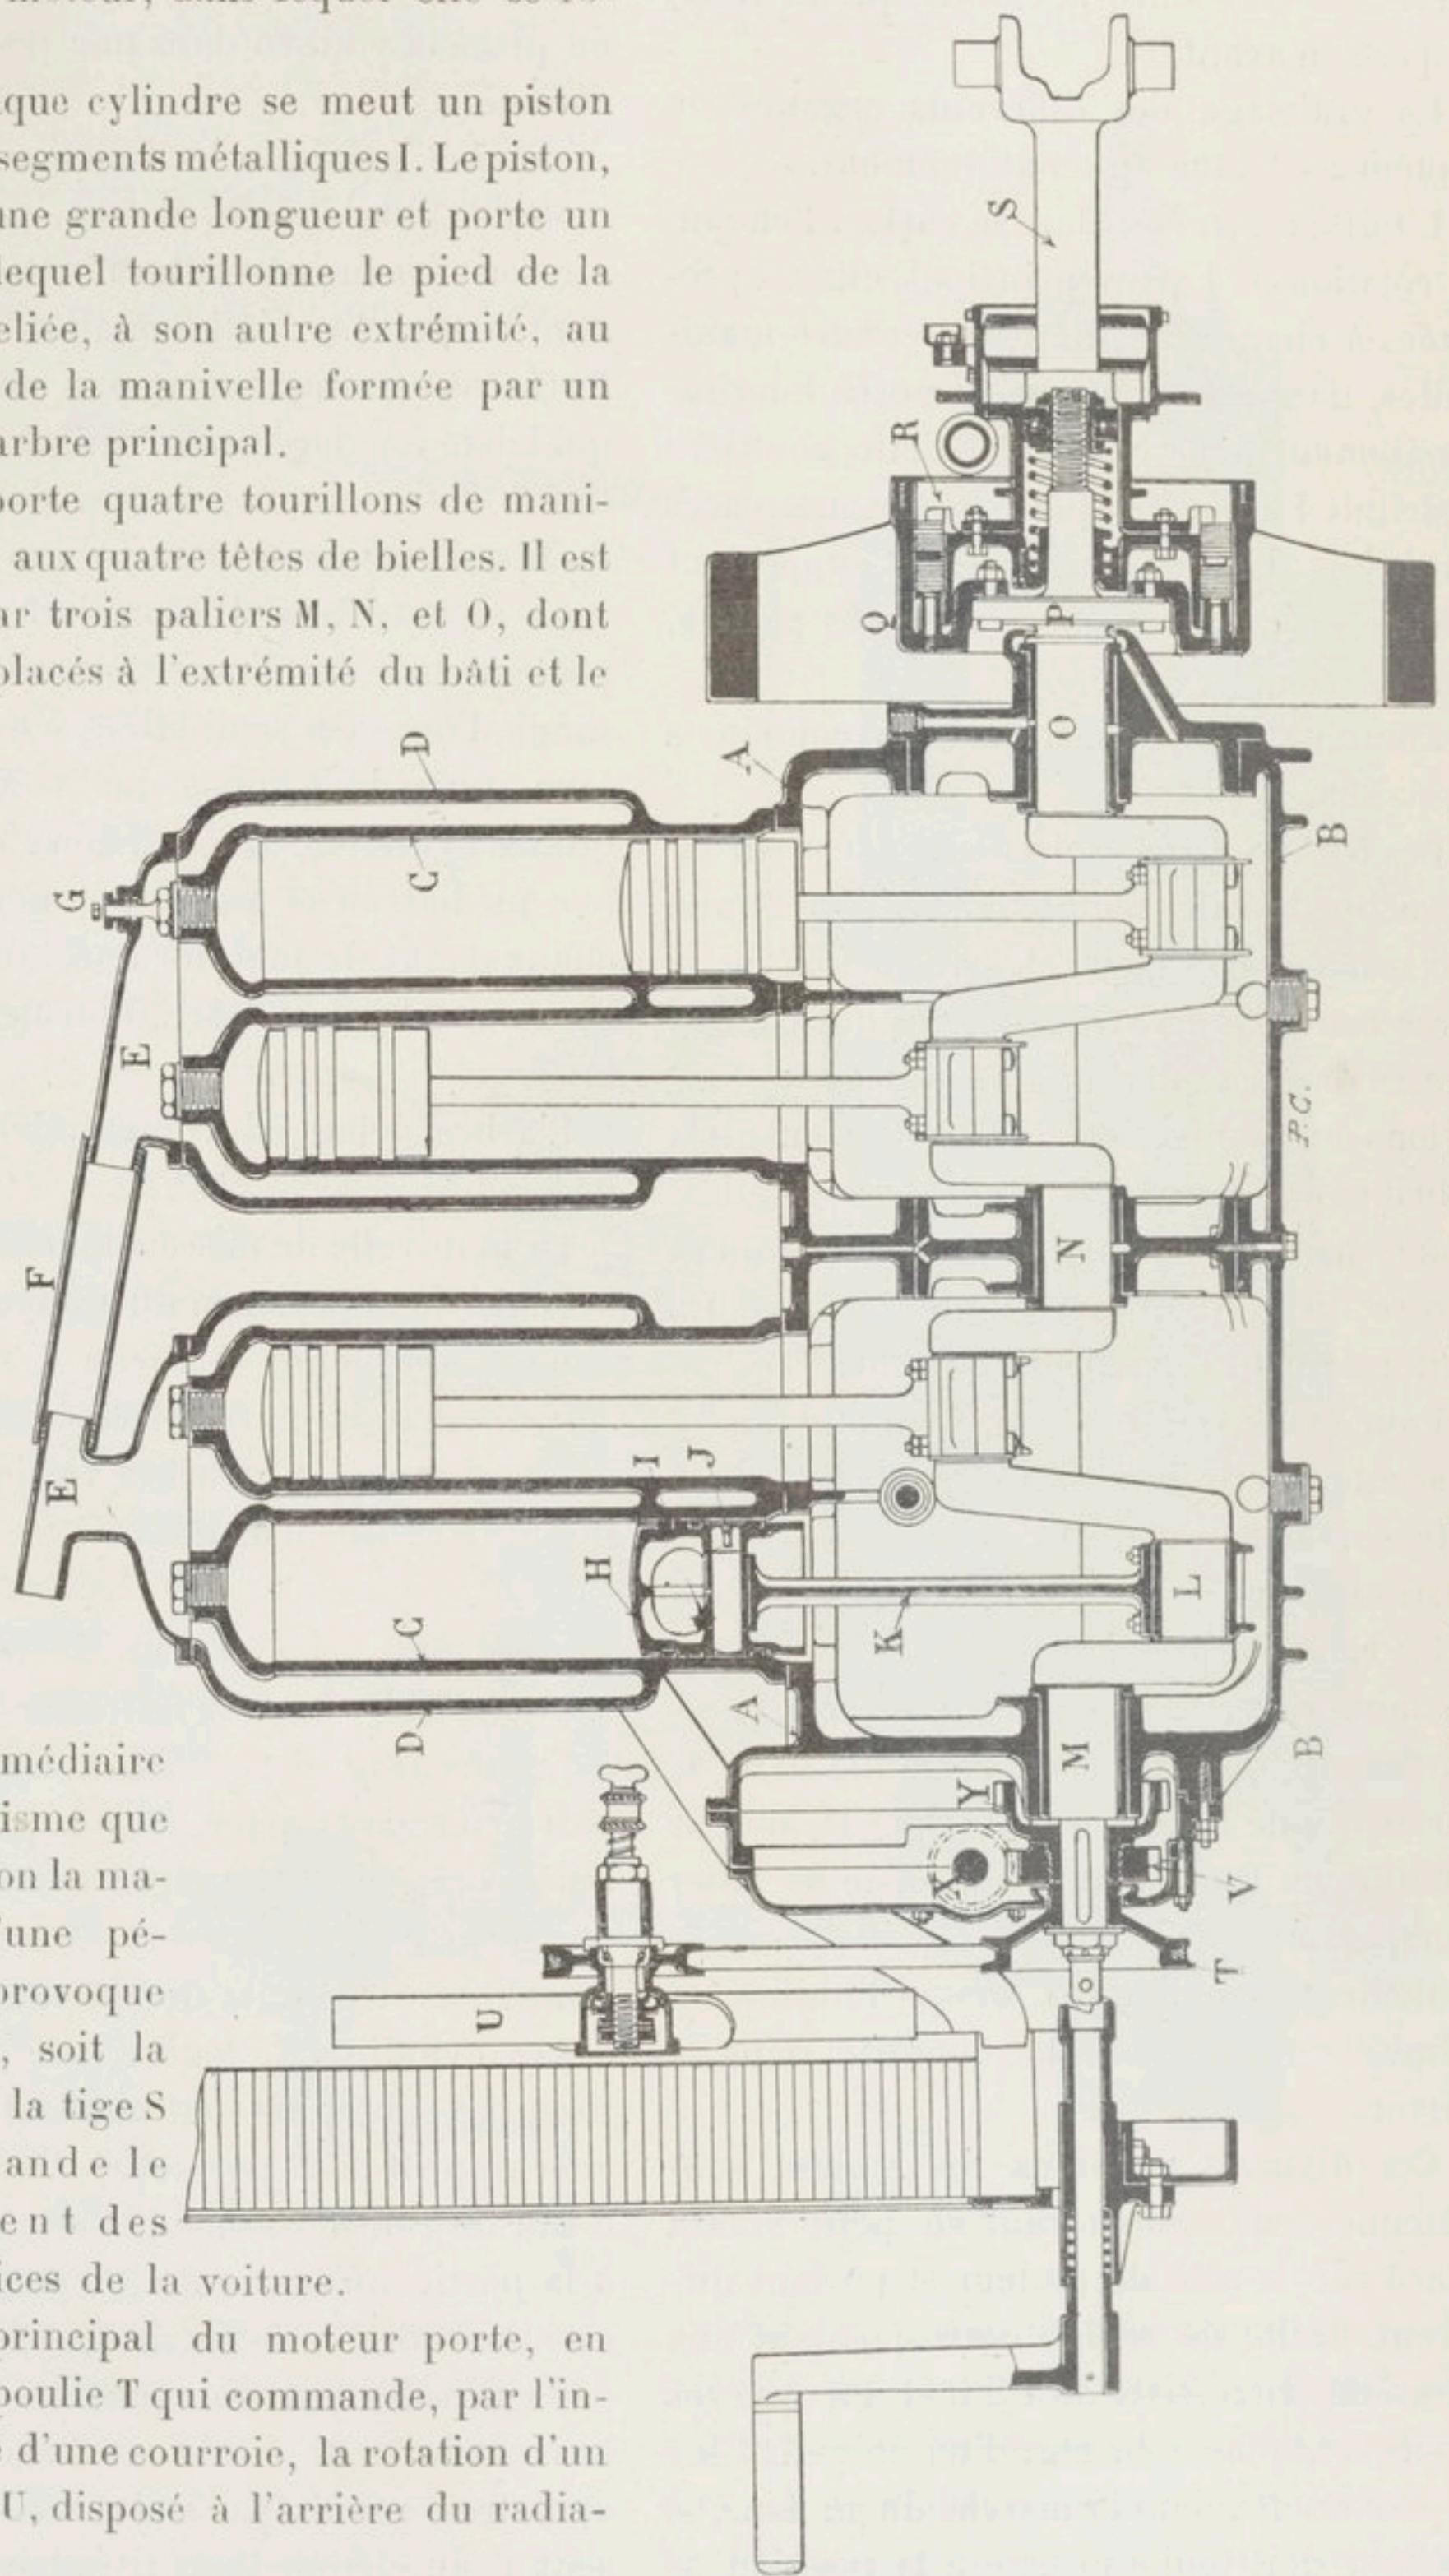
Coupe du moteur d'automobile Brasier à quatre cylindres.
